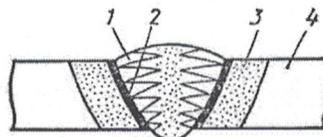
Сварное соединение: 1 – сварной шов; 2 – зона сплавления; 3- зона термического влияния; 4- основной металл.
